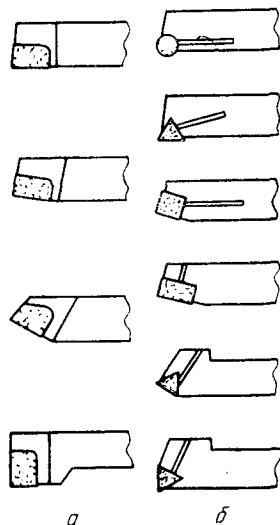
Токарные резцы с напаянными твердосплавными пластинками (а) и механическим креплением пластинки (б)
